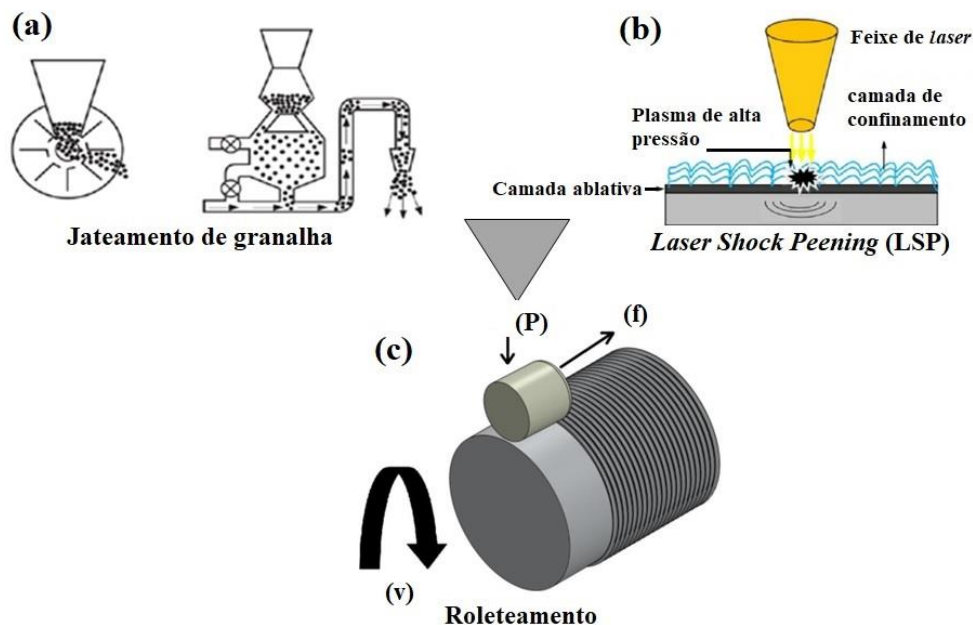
Técnicas de tratamento mecânico de superfícies: a) jateamento de granalha, b) laser shock peening e c) roleteamento
